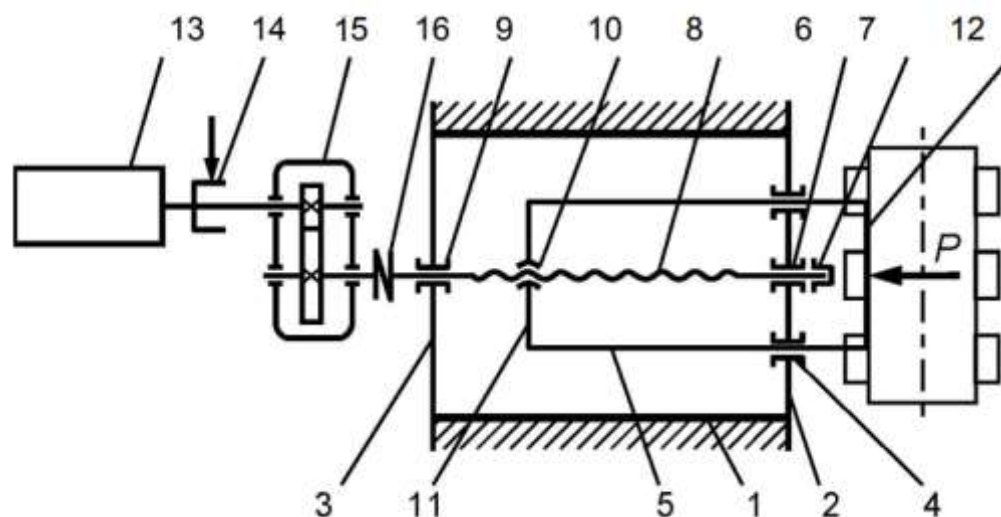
Схема винтового толкателя: 1 - рама неподвижная;
